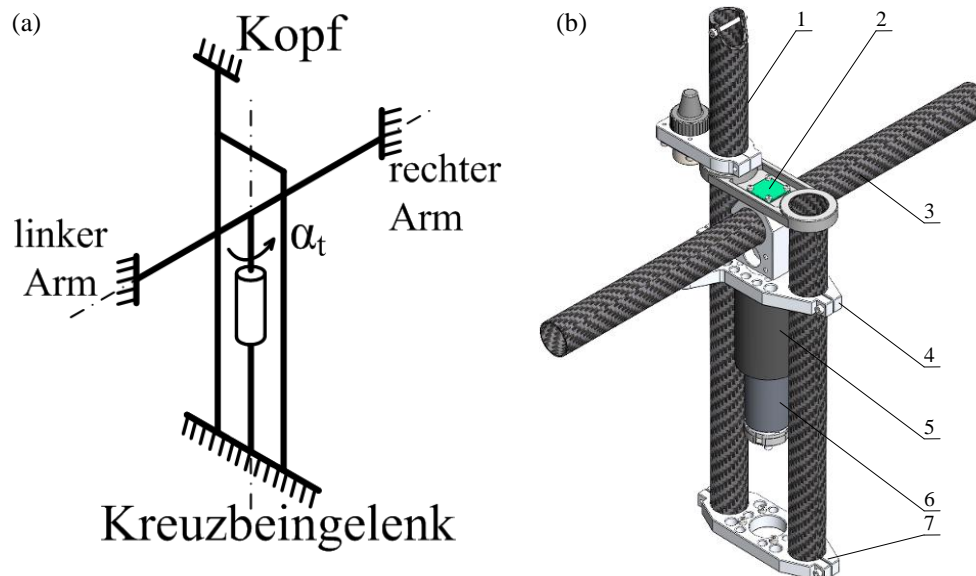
Konstruktion des Brustgelenks: a – Kinematik des Kreuzbeingelenks; b – CAD-Entwurf (1 – Hals, 2 – magnetischer Winkelsensor, 3 – Kohlefaserrohr des Schlüsselbeines, 4 – Befestigungselement der Schulter, 5 – Getriebe, 6 – Synchronmotor, 7 – Befestigungselement für die Ankopplung des Kreuzbeingelenkes)
